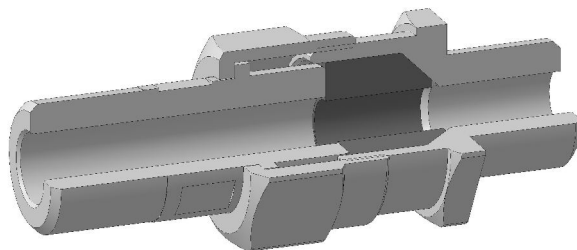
Конструкция кабельного ввода ВН с фитингом для монтажа кабеля в трубе
